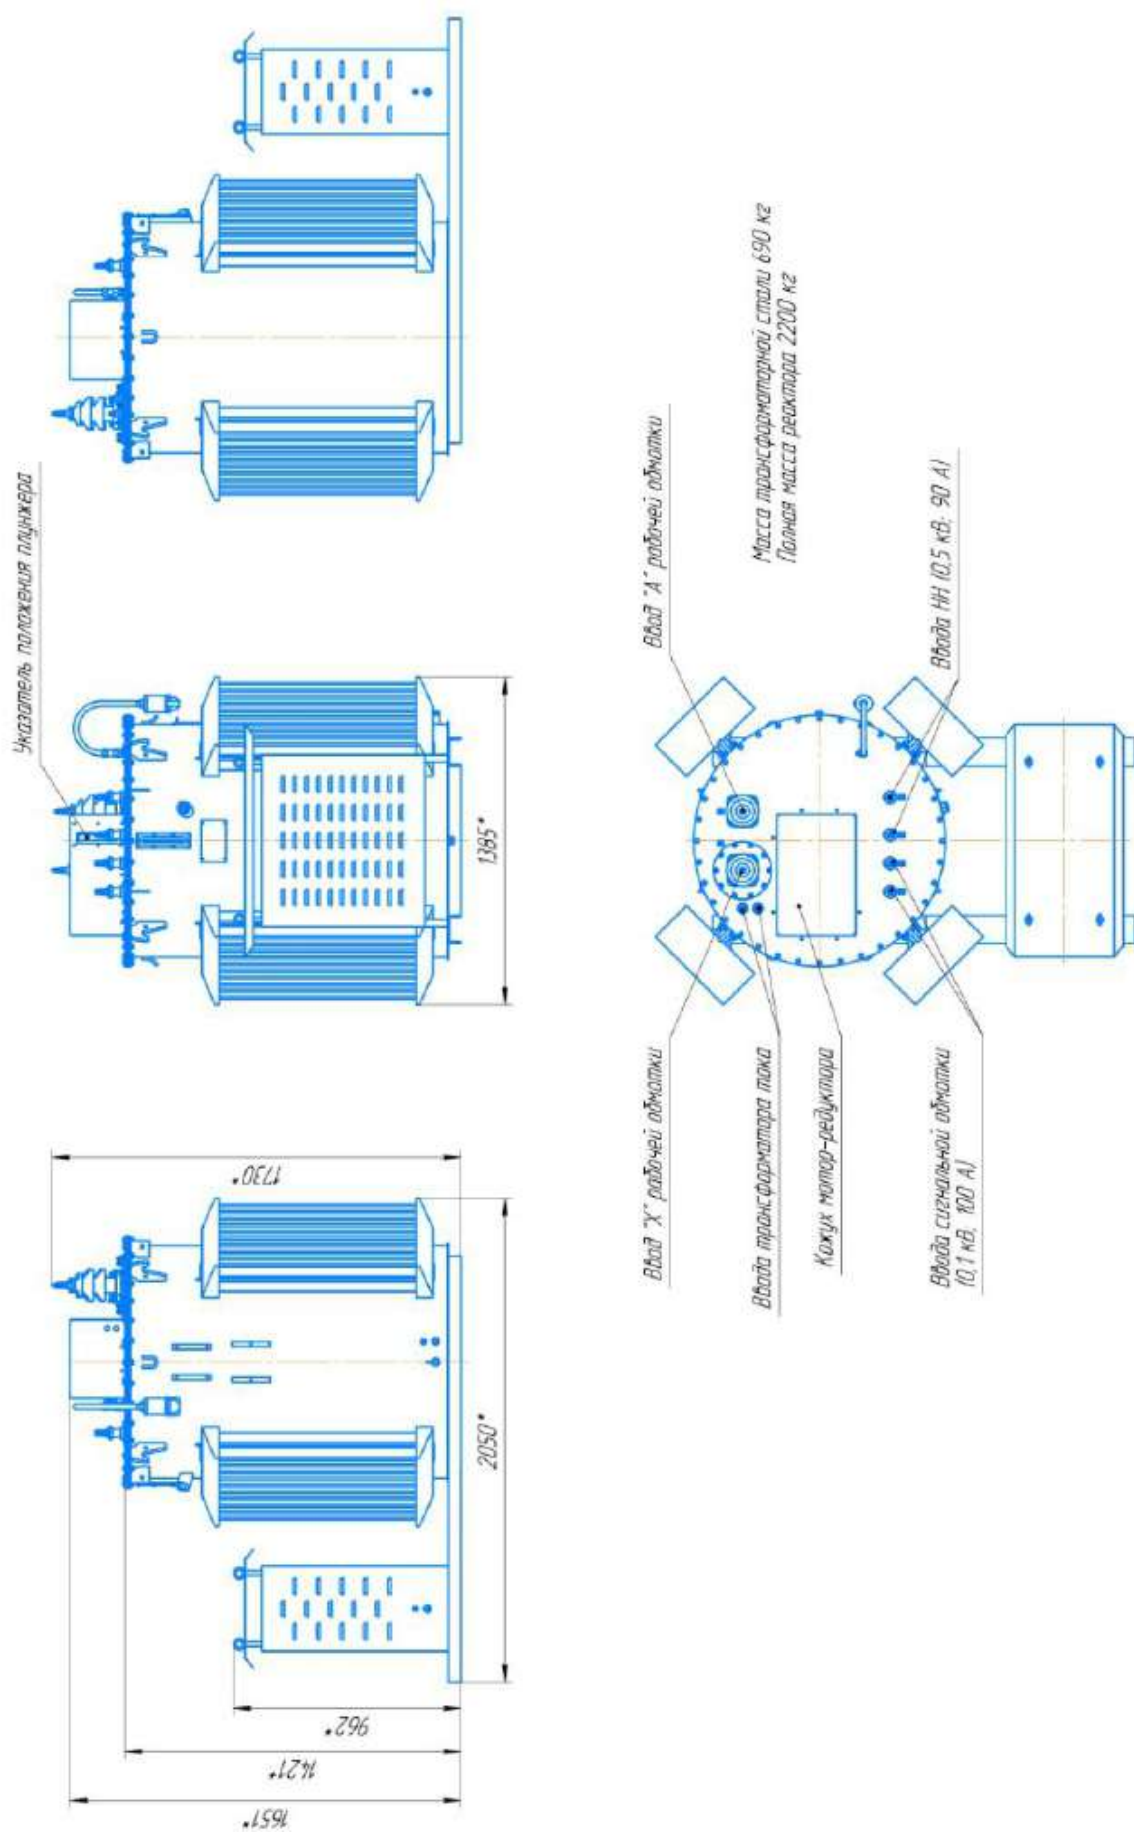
Общий вид дугогасящего реактора РДМРА с регулируемым резистором РЗН
